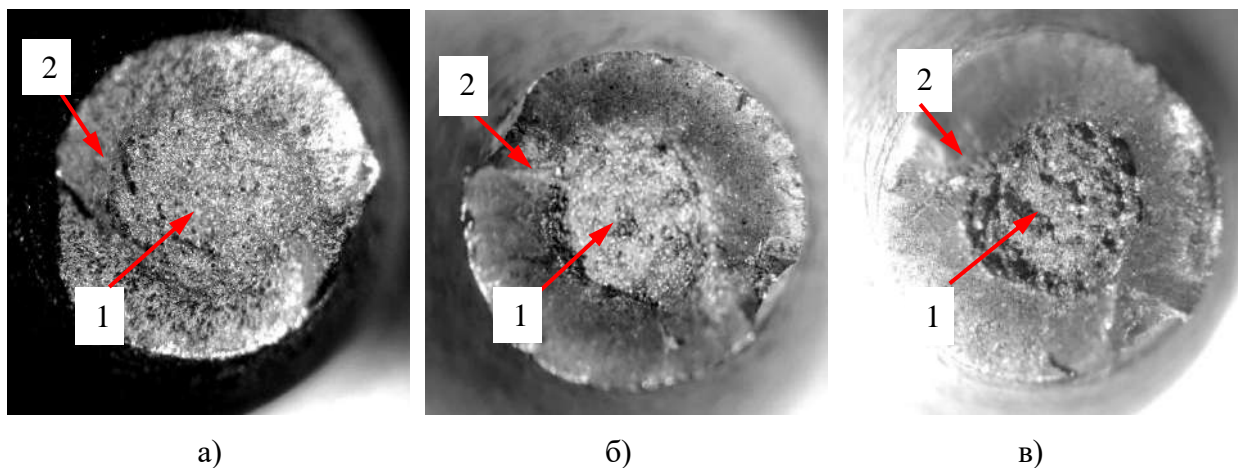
6 Макроизображения поверхностей изломов разрывных образцов: а – образец ЖТ8, б – образец ЖТ16, в – образец М. Стрелками показаны: 1 – площадка нормального отрыва, 2 – зоны среза.
